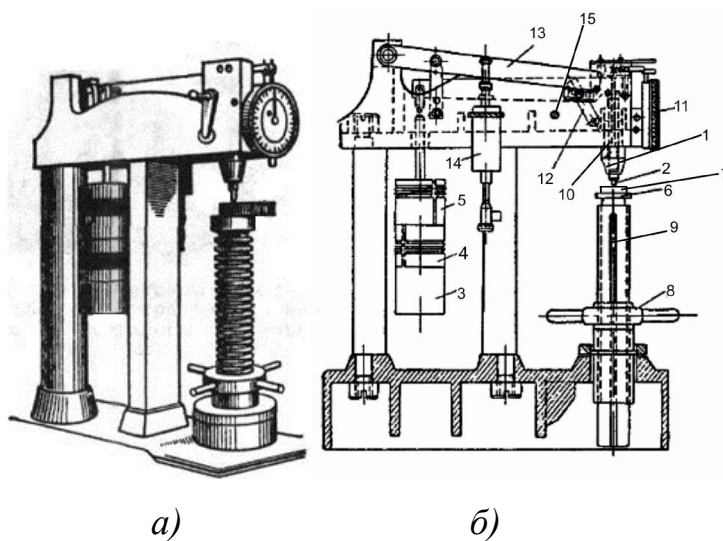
Прибор типа Роквелла: а — общий вид; б — схема
